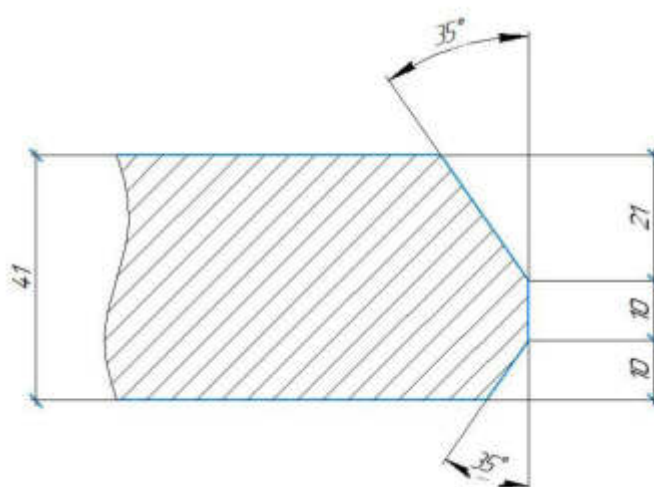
Фаски для сварки двумя дугами
